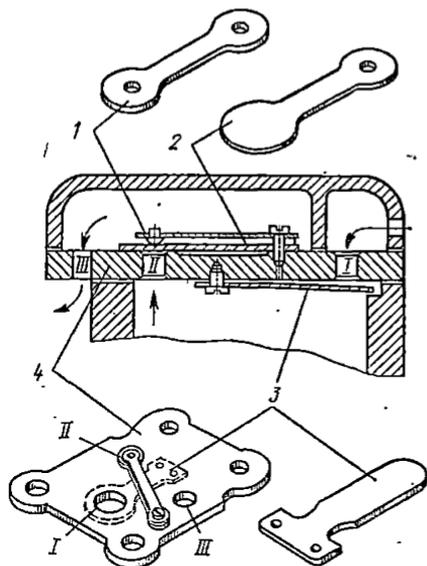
Клапанная группа компрессора ФГО,7 ~ 3:
